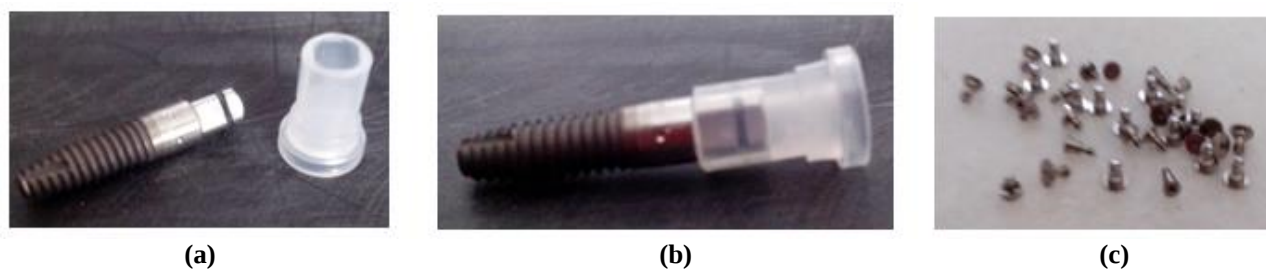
Montagem Frasco de Implante Dentário. (a) implante montador com montador e parafuso montador e tampa de frasco interno; (b) montagem do conjunto implante com a tampa interna; (c) tapa implante – Fonte: SISTEMA INP (dados internos).
